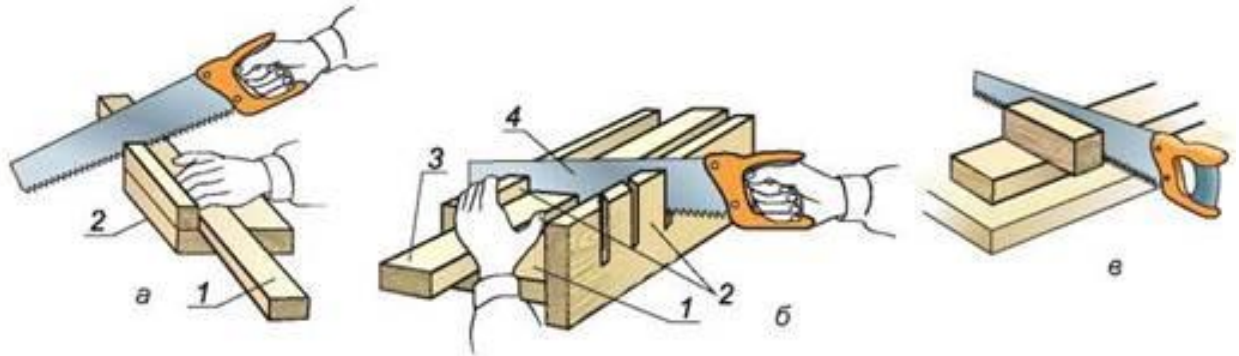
Прийоми пиляння: а – з упором (1 – заготовка, 2 – упор); б – пиляння в стуслі (1 – дно, 2 – бокові стінки, 3 – заготовка, 4 – пилка); в – запилювання з брусом
